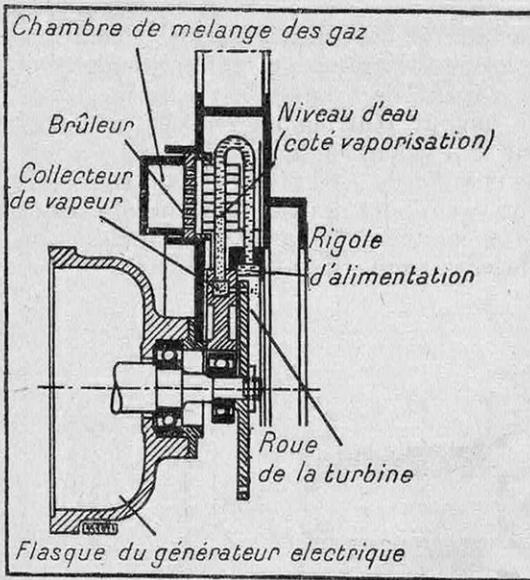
COUPE DE LA PREMIÈRE TURBINE HUTTNER DE 0,28 CH
